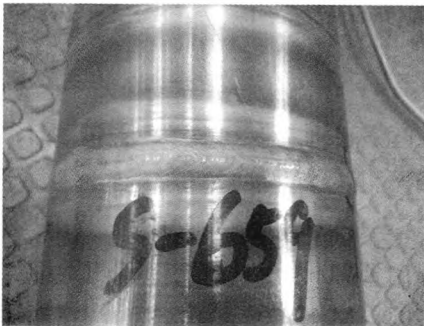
S-659 焊丝所焊试验件的焊缝表面
